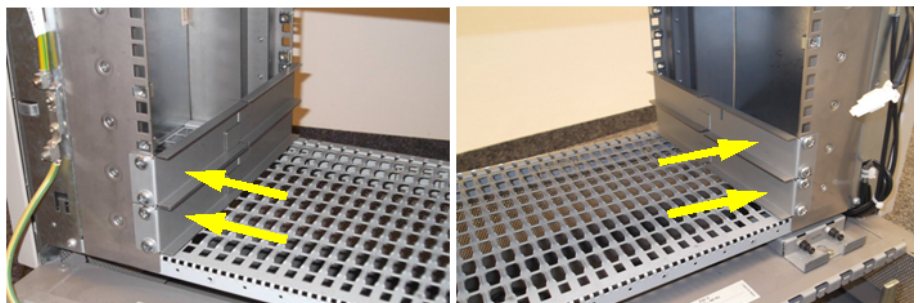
Montaggio della piastra di ventilazione (lato posteriore)
